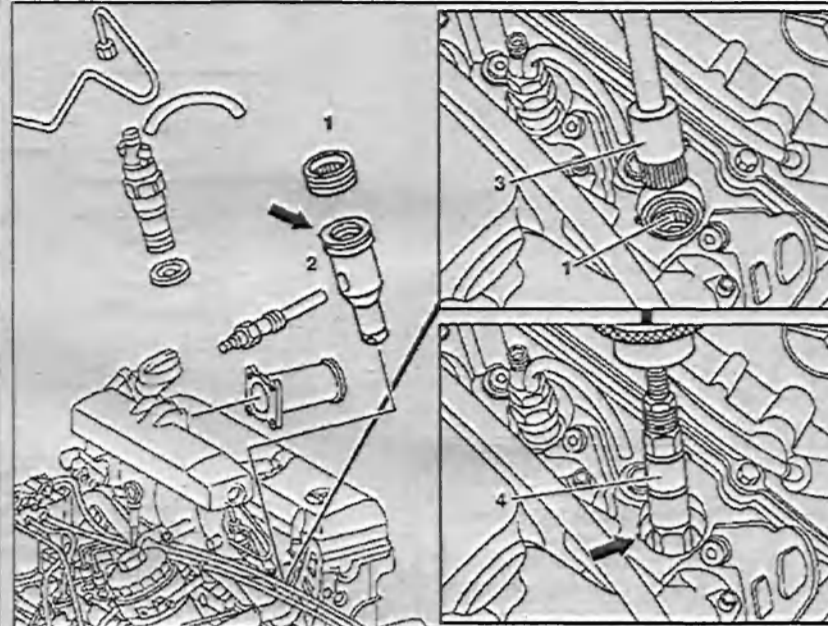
Снятие и установка предкамеры (двигатели 601.943): 1 - Резьбовое кольцо; 2 - Предкамеры; 3 - Приспособление; 4 - Съемник.
